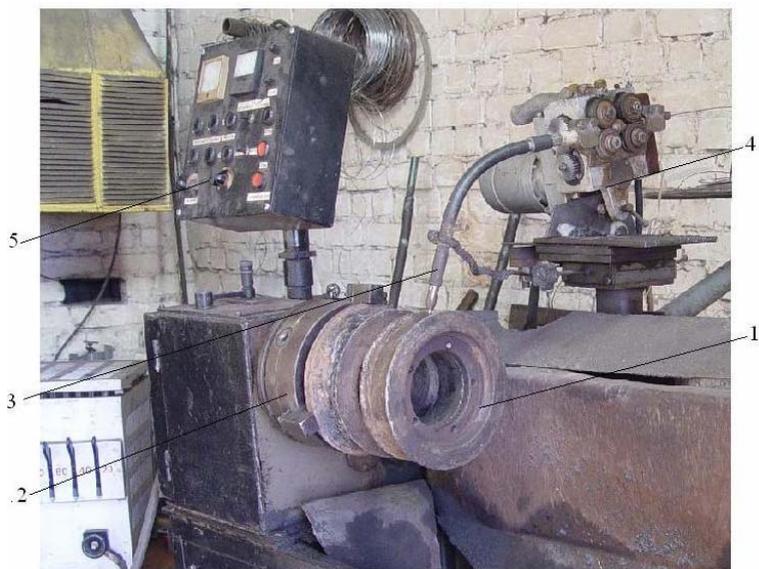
Наплавка опорного катка гусеничного трактора порошковой проволокой на установке УД-209: 1 – каток; 2 – зажимной патрон; 3 – горелка; 4 – подающий механизм; 5 – пульт управления
